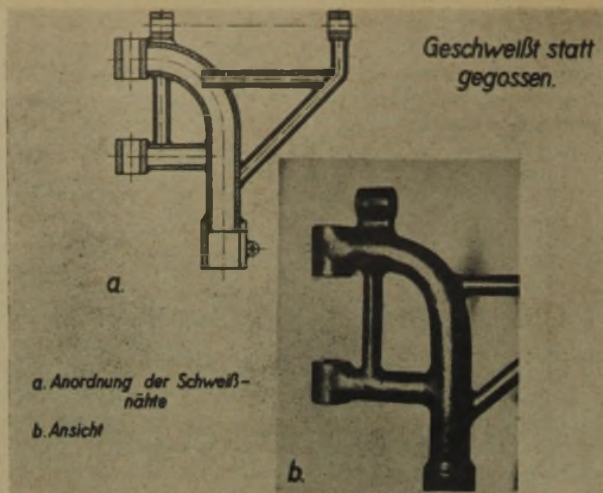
OberTeil einer Säulenbohrmaschine aus Stahlrohren — autogen geschweißt
